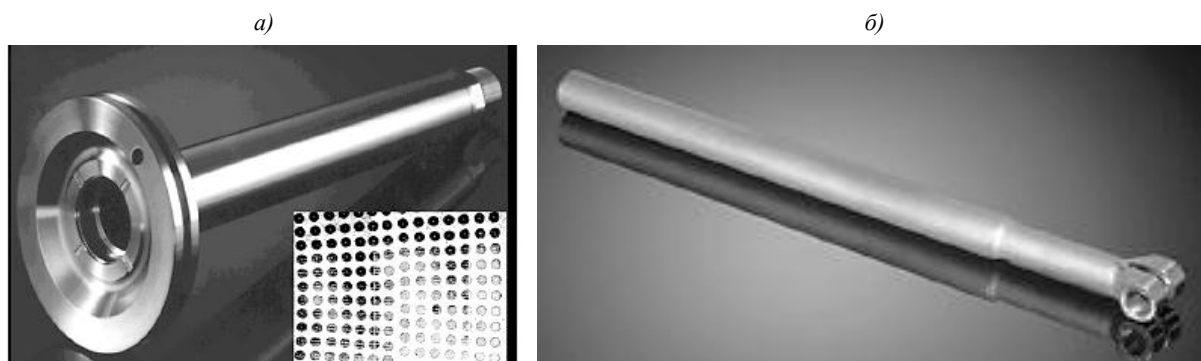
Поршень приводного механизма сопла ГТД PWF119 (а)
